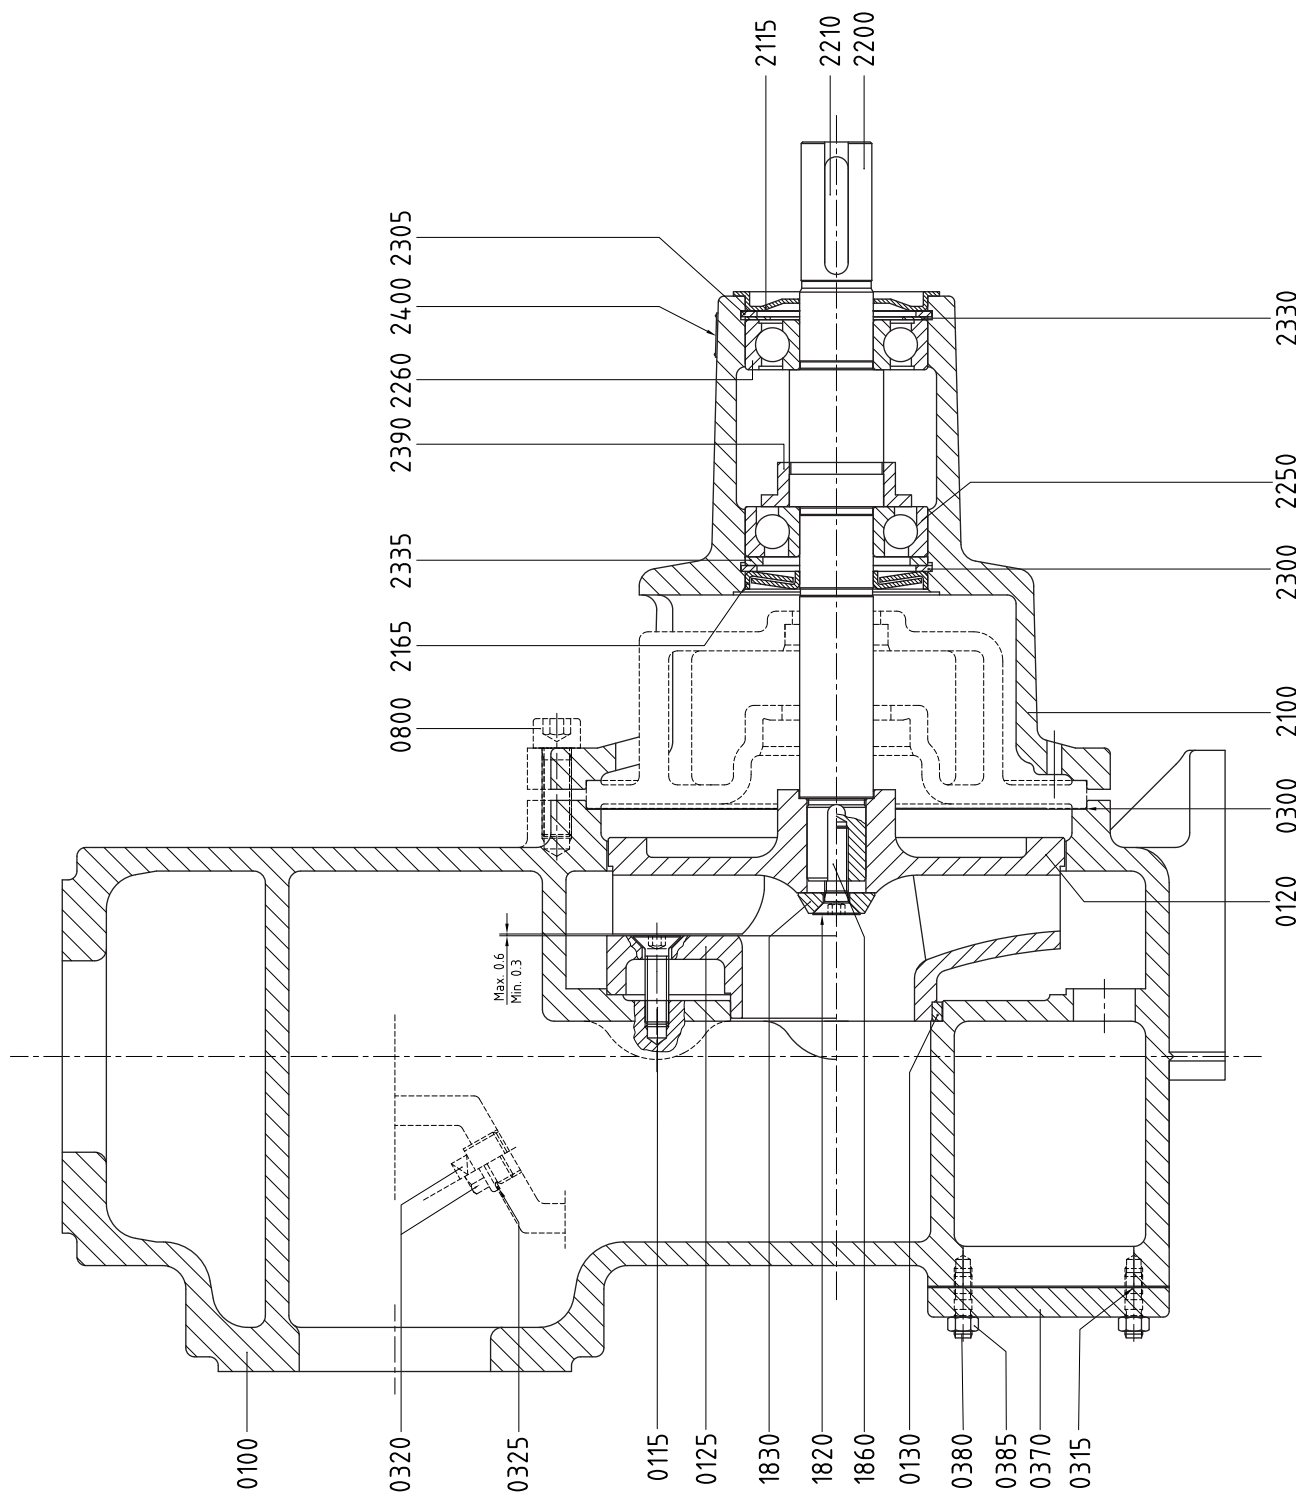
Desenho em corte FRE - grupo de rolamento 2.
